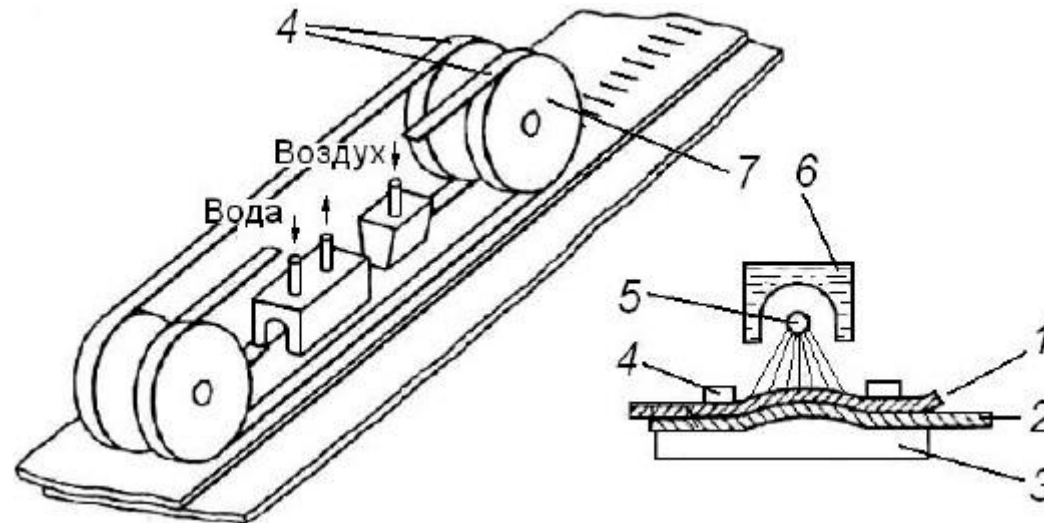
Схема сварочной головки для непрерывной сварки пленки ИК-излучением: 1,2 – свариваемые пленки; 3 – подложка; 4 – стальные ленты; 5 – источник ИК-излучения; 6 – рефлектор; 7 – прижимные ролики
